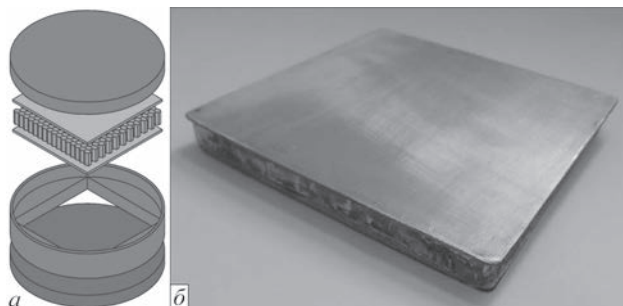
Схематическое изображение оснастки с элементами панели (а) и вид трехслойной сотовой панели после сварки (б)
